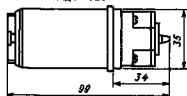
Габаритные и установочные размеры двигатель-тахогенератора АДТ-329
